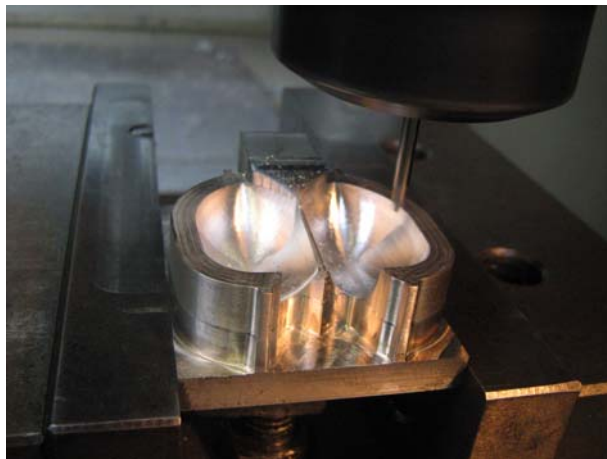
Maquinado álabe Pelton en Fresadora C.N.C
